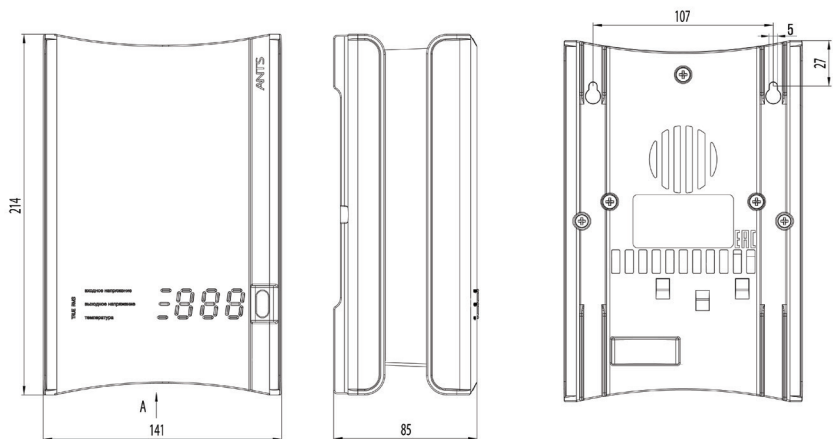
Габаритные и установочные размеры стабилизаторов КилоГерц 1-3 и 1-6
